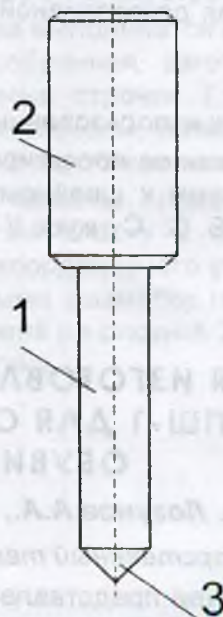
Инструмент для выполнения разметки пластин кассеты
